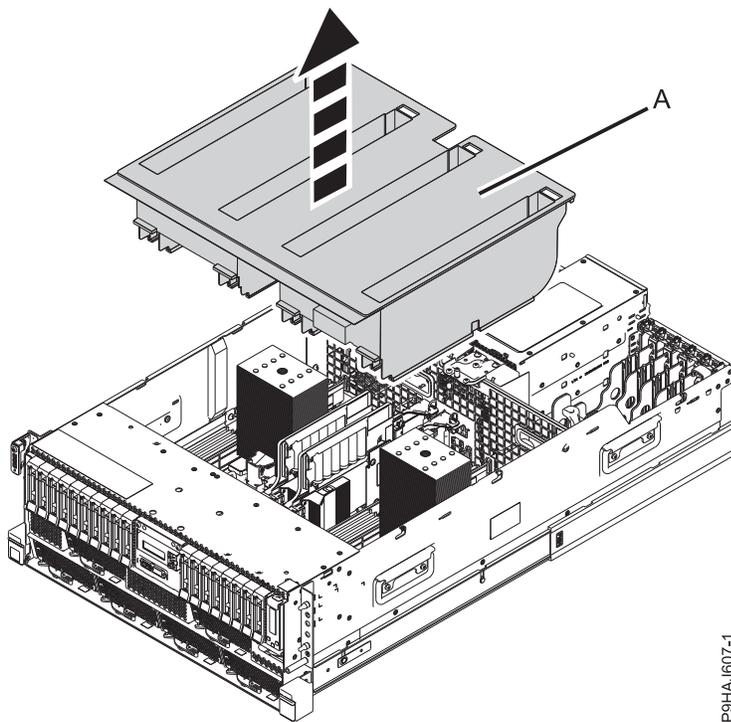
Removendo a placa defletora de ar de um sistema montado em rack
